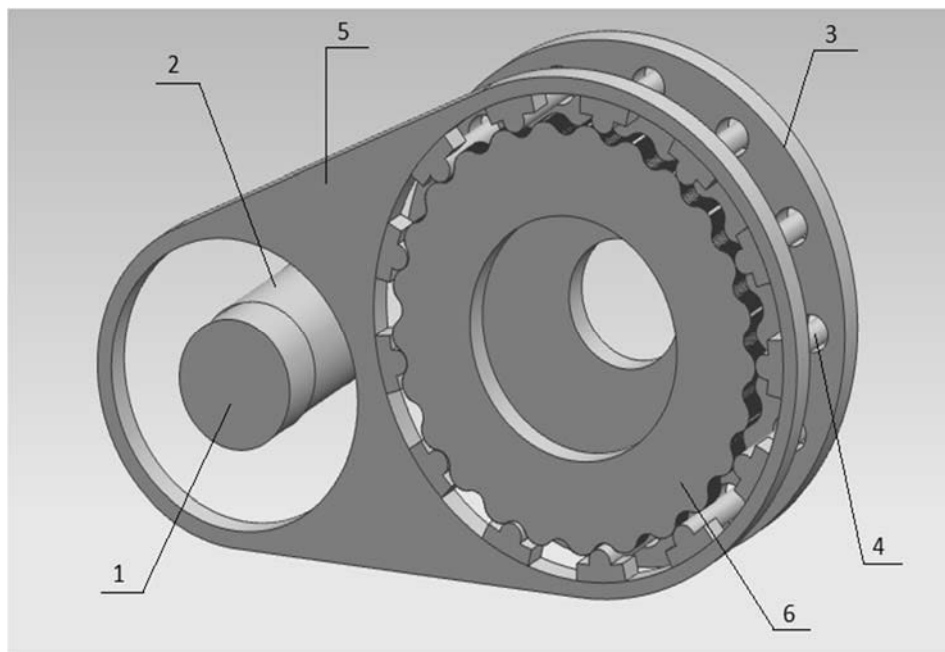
Общий вид эксцентриковой передачи с параллельным расположением входного и выходного валов с одним потоком мощности: 1 – эксцентрик; 2 – входной вал; 3 – сателлит; 4 – ролик сателлита; 5 – неподвижный диск; 6 – центральное колесо
